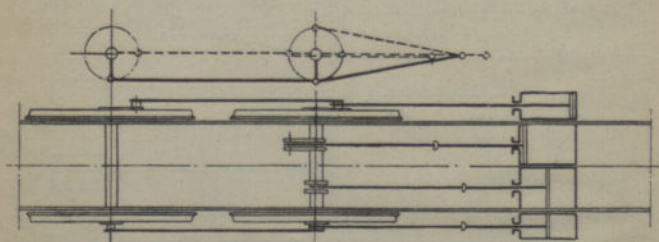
Mechanismo motor de locomotiva compound de 4 cilindros.
